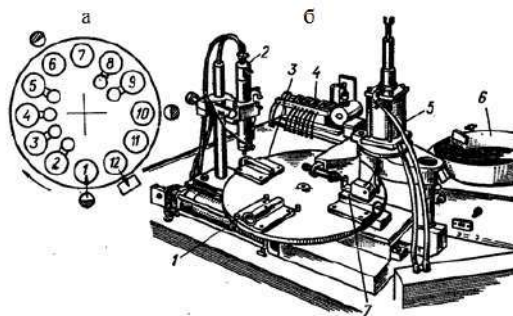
Схема работы сборочного полуавтомата с круглым столом: а - примерная схема сборки на полуавтомате: 1 - позиция для ручной загрузки базовой детали; 2, 3, 4, 5, 8, 9 - сборочные позиции, на которых производятся автоматически подача деталей из бункеров и сборка; 6 - 10 - позиции для ручной сборки; 7 - позиция для автоматического контроля сборки; 11 - позиция для автоматической продувки и смазки; 12 - съем собранного узла; б – сборочный полуавтомат с круглым столом.
